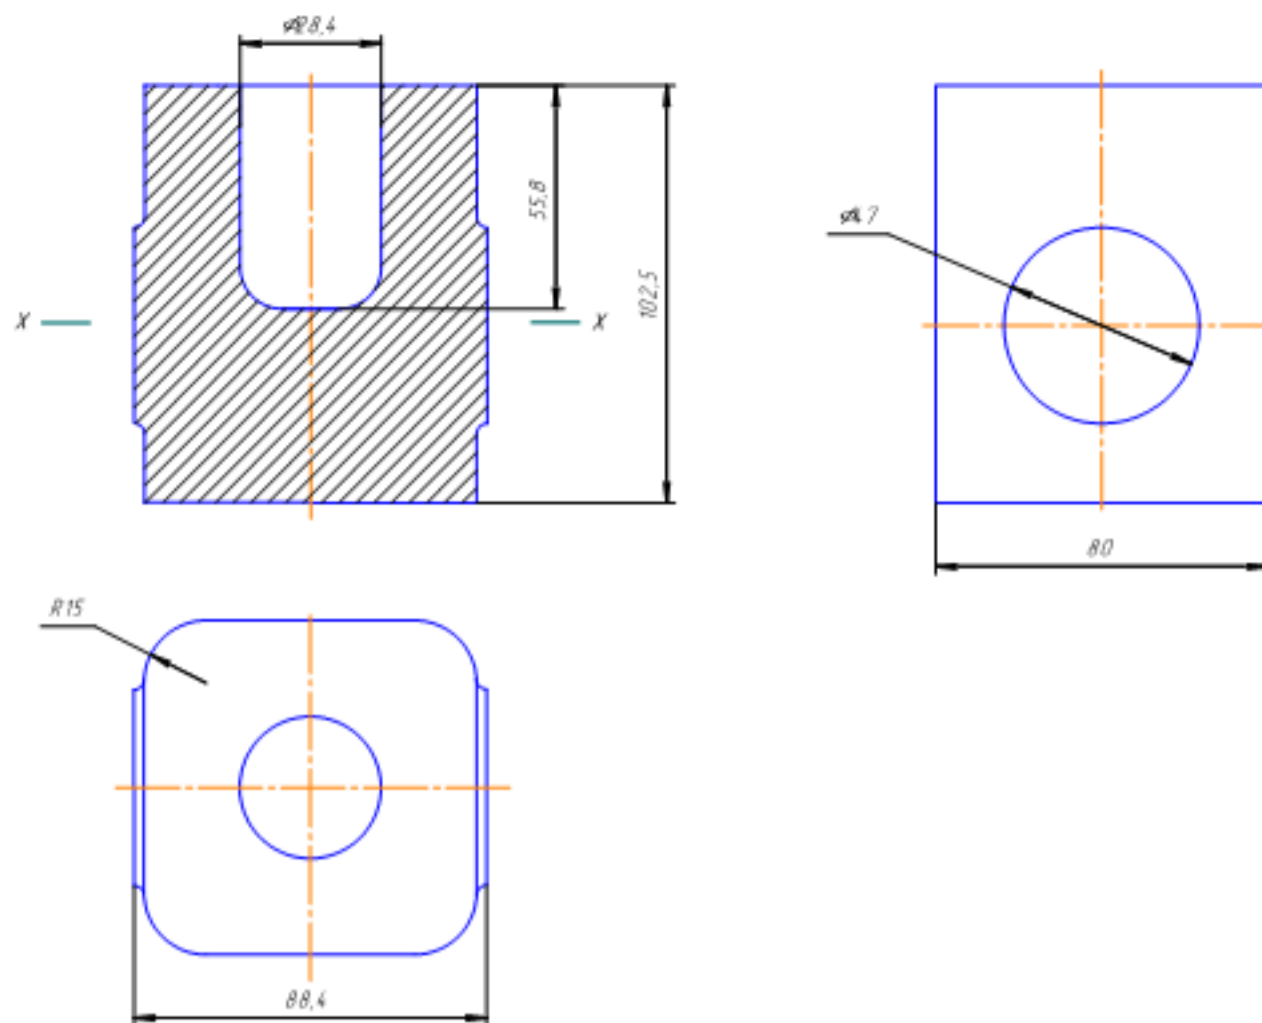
Ескіз заготовки одержаної литтям в піщано-глинисті форми
